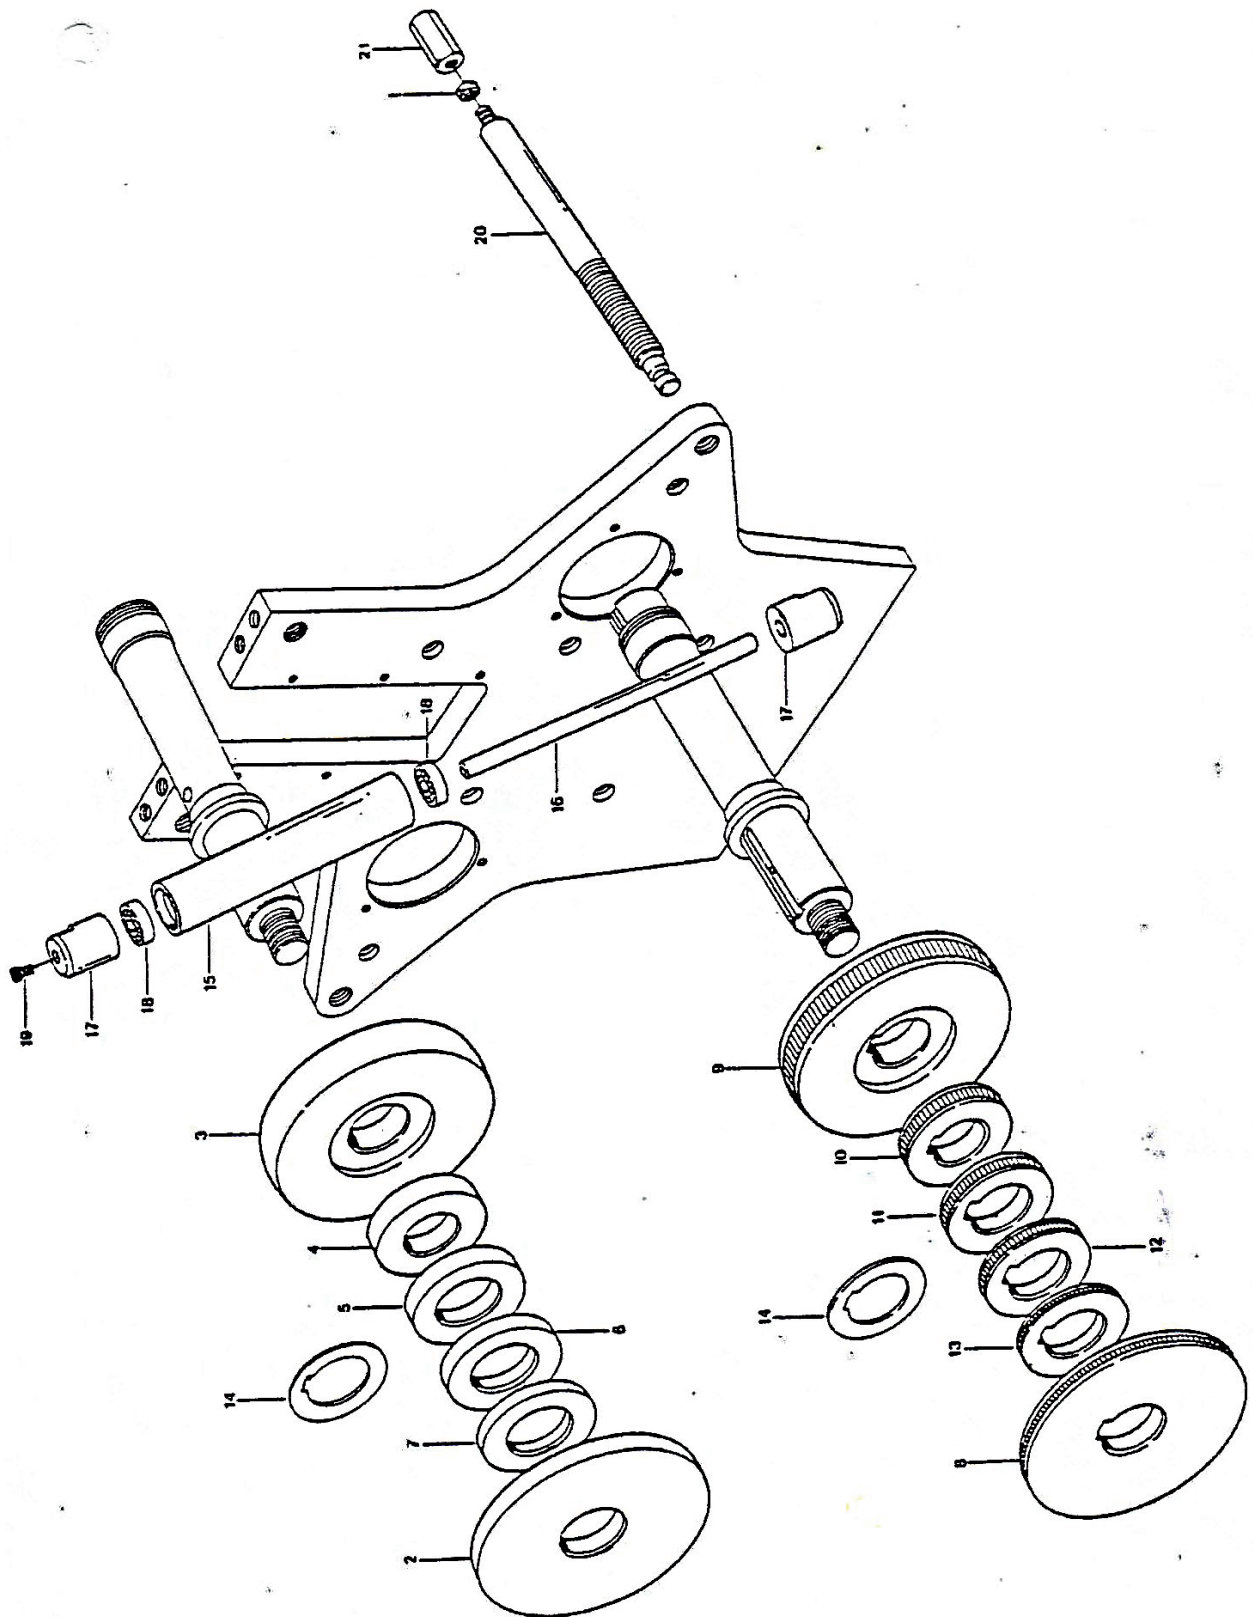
Dessin des pièces détachées 3 PRM 60 FH
